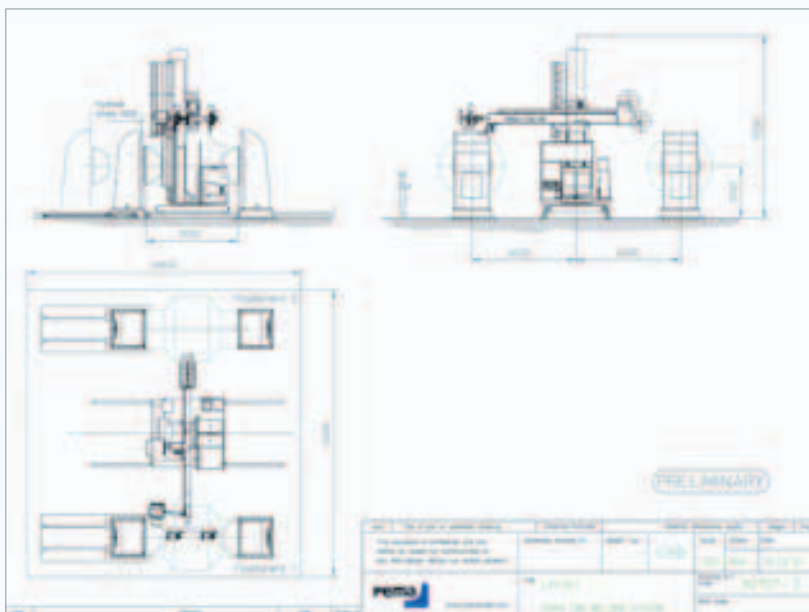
Планировка участка для изготовления шаровых кранов и шиберных задвижек. Одна сварочная станция обслуживает 2 рабочие зоны
